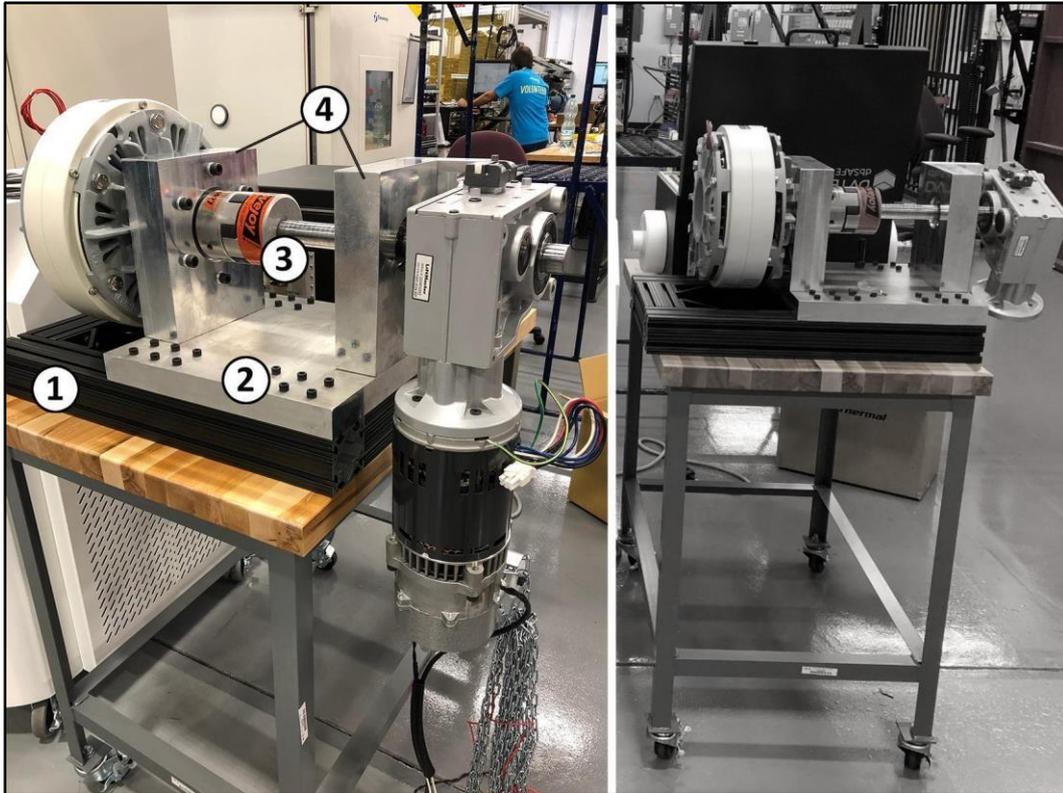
Fixture modular: 1) Perfiles de aluminio fijos a la mesa de trabajo; 2) Base butcher; 3) Acoplamiento de acero; 4) Bloques de montaje para magbrake y abridor
